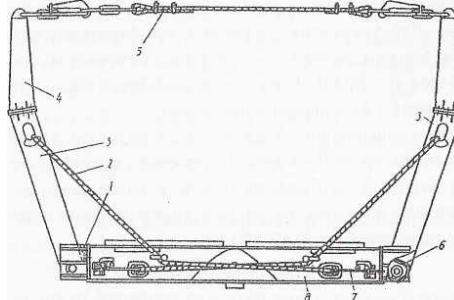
Коник автомобіля : 1 - упор стійки; 2 — канат стійки; 3 — стійки; 4 — наконечник стійки; 5 — канат страхувальний; 6 — канат механізму полегшення підйому стійок; 7 - запор каната стійки; 8 — основа коника
